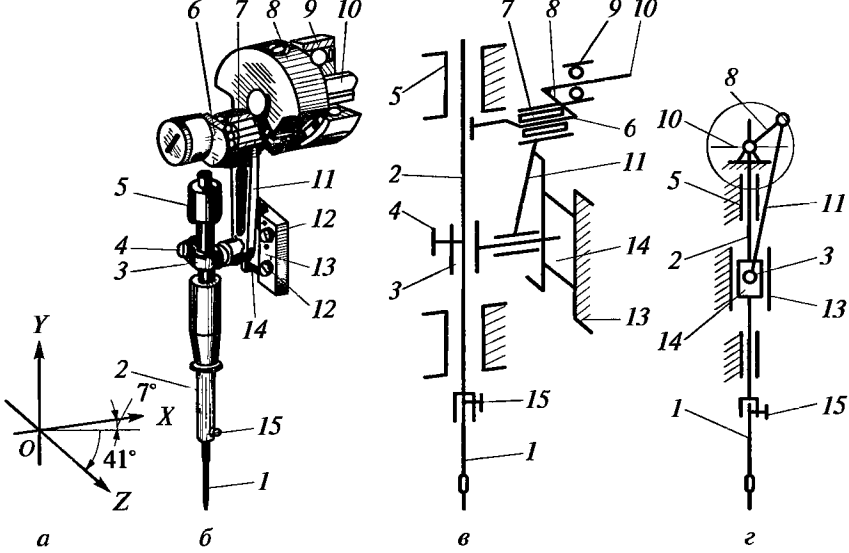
Виды схематического представления механизма иглы швейной машины челночного стежка:
